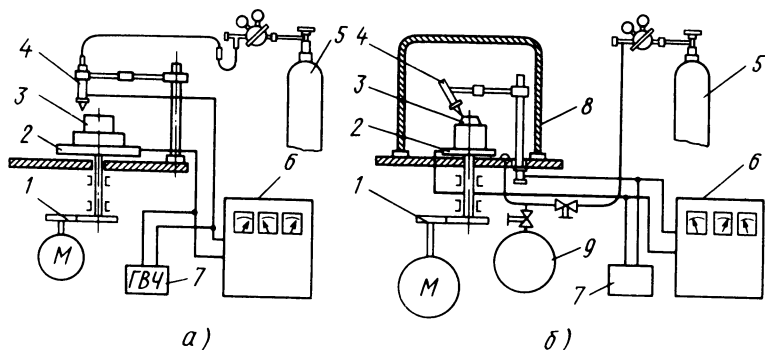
Установки для аргонодуговой сварки:
